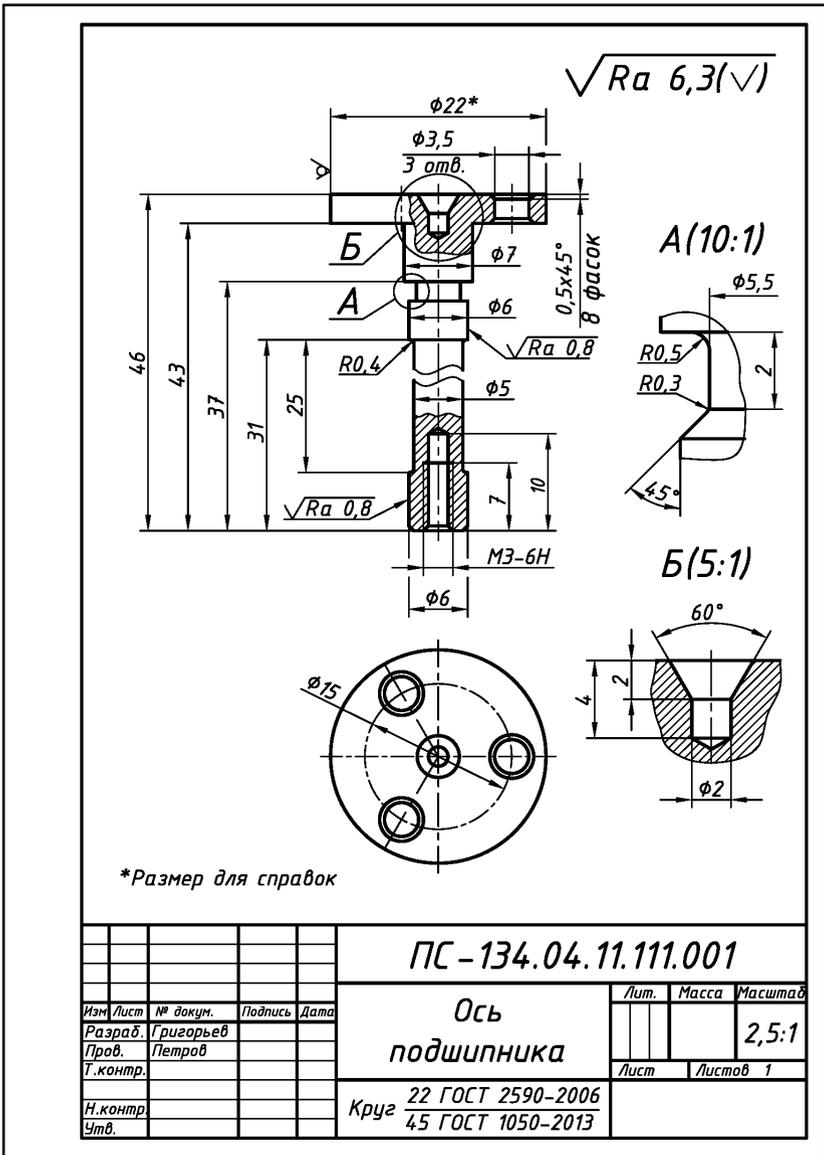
Оформление рабочего чертежа точеной детали из металла
